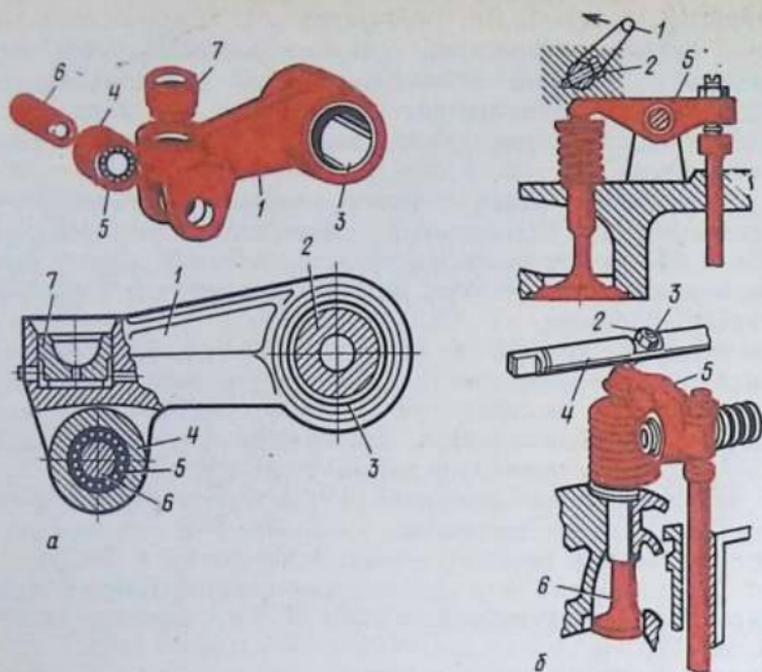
Толкатель и декомпрессионный механизм дизеля А-41:
